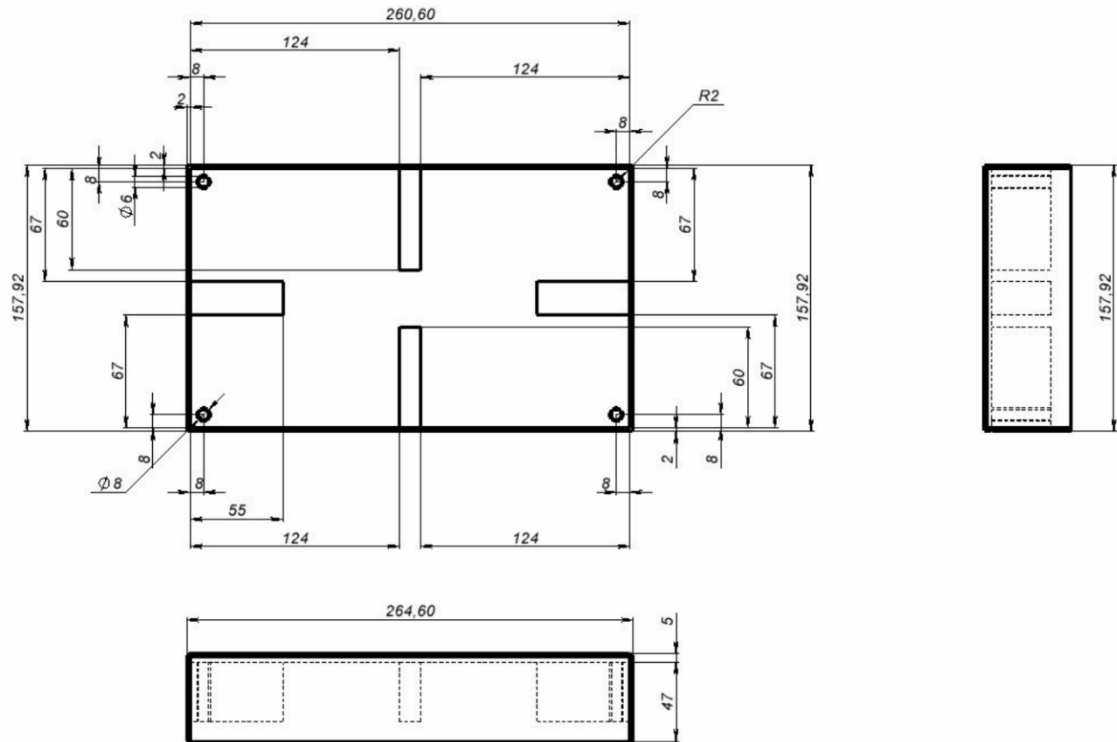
Фрагмент креслення основи корпусу лабораторного макету
